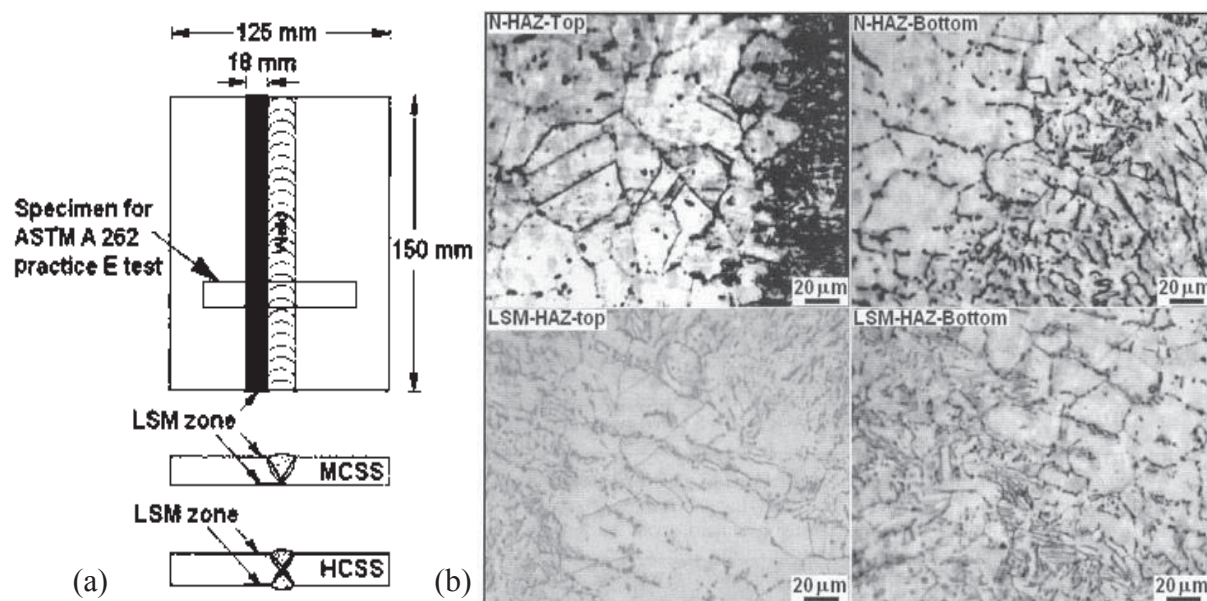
(a) Representación del procesos de soldadura y tipos de unión utilizadas en el proceso de soldadura (b) micrografías del AIA 304 sin tratamiento en la parte superior en la ZAT y la parte superior e inferior donde se aplico la fusión con laser. Reportando el incremento de resistencia a la corrosión debido a la discontinuidad de la red de carburos notorios en ambas partes de la probeta en tanto en la parte inferior como en la parte superior.
